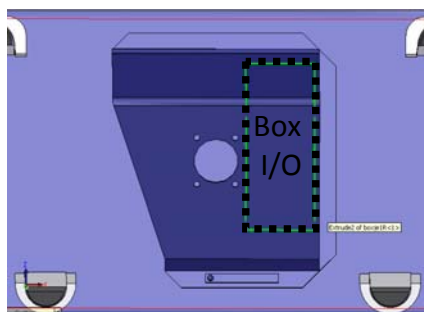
Zijanzicht pootjes H (gekozen, vier half cilindrische schuin lopende poten)
